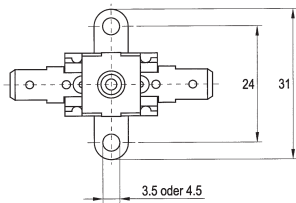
Flansch mit doppelseitigem Befestigungslappen
